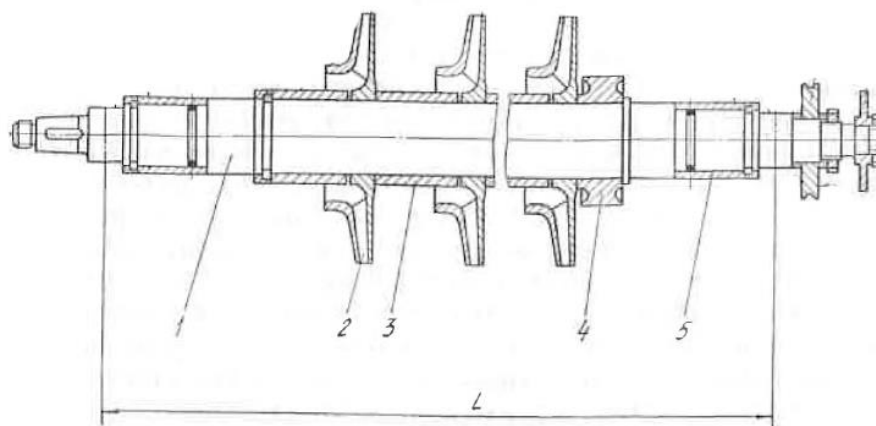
Конструкция ротора с межопорным расположением рабочих колес:
